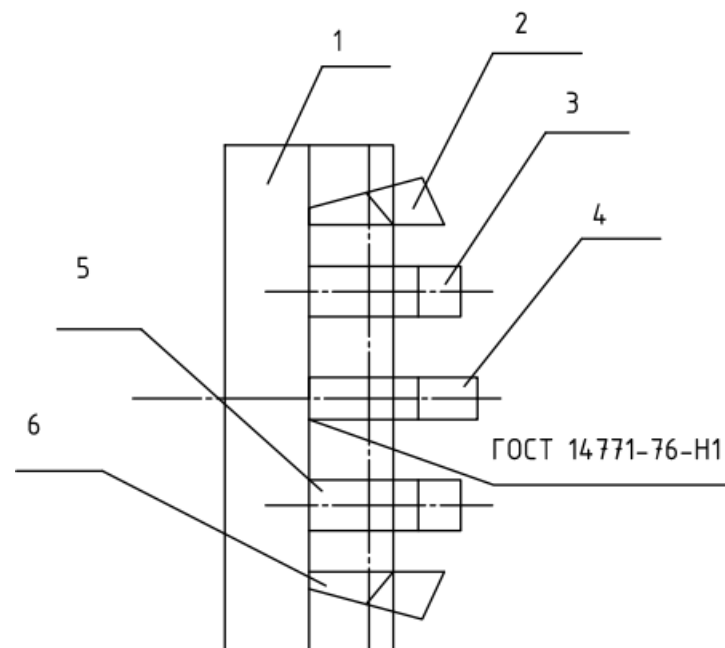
Складання і зварювання гребінки і зубів.
